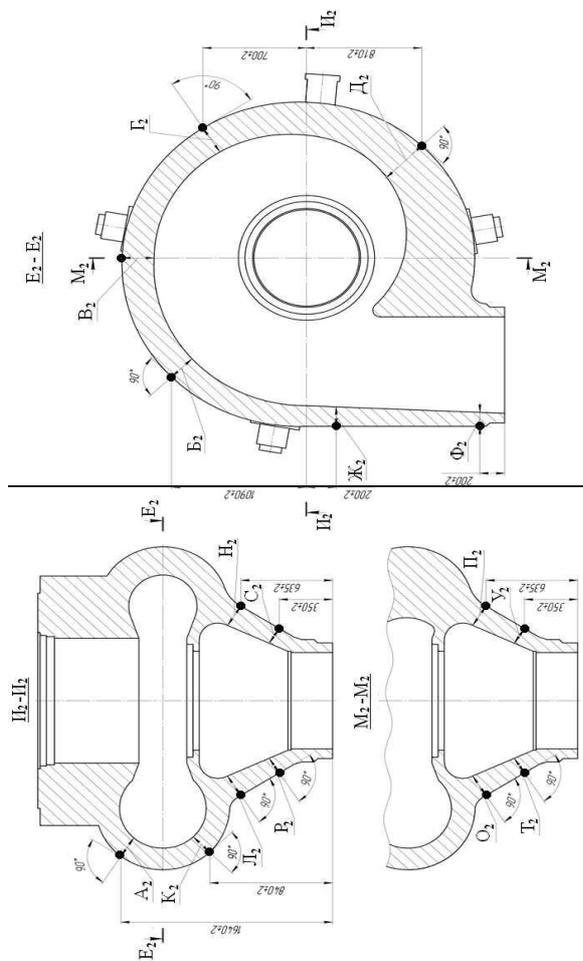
Схема зон контролю твердості металу ГЦН. Основний метал корпусу равлика насоса з боку зовнішньої поверхні
